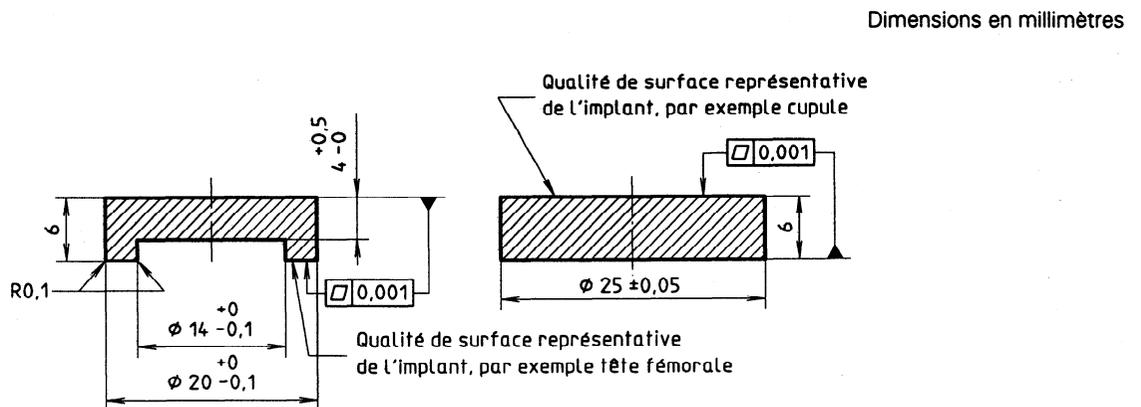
Géométrie des éprouvettes annulaire et discoïdale et définition des dimensions nécessaires
